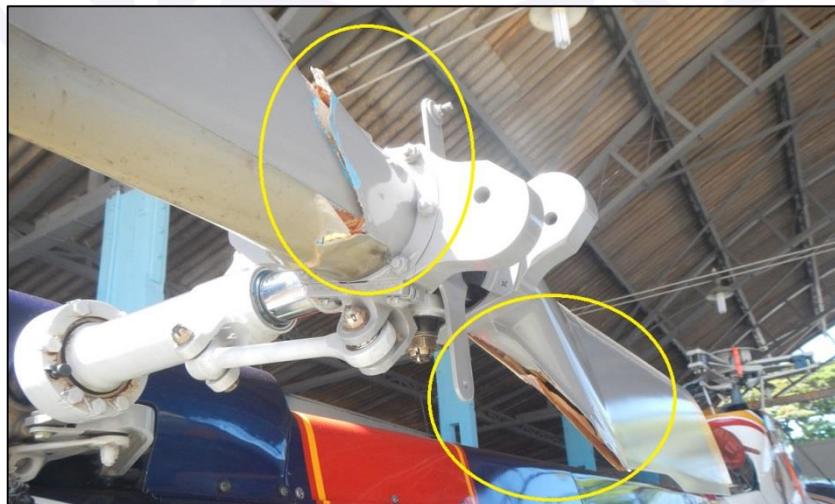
Detalhe dos danos ao conjunto do rotor de cauda.
